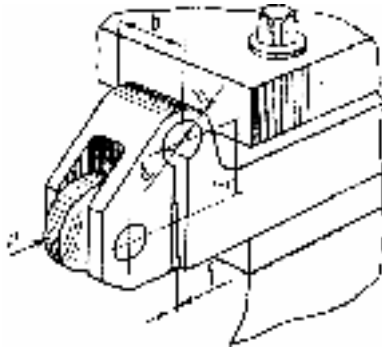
Пристрій для обкатування деталей роликми з пруживним корпусом:
